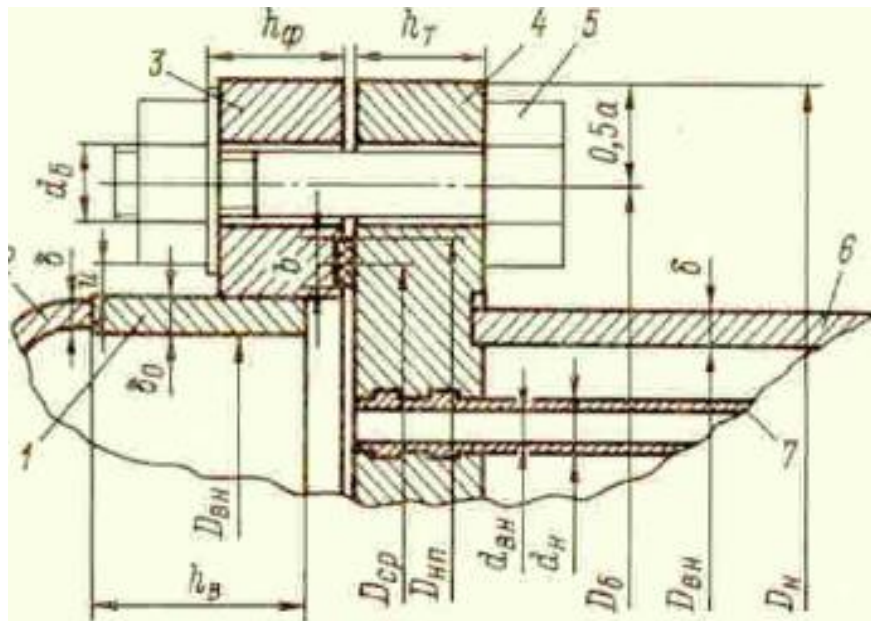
Фланцеве з'єднання: 1-втулка фланця; 2-днище кришки; 3-плоский приварний фланець кришки; 4-трубні ґрати; 5-болт; 6-обічайка; 7-теплообмінна труба.
